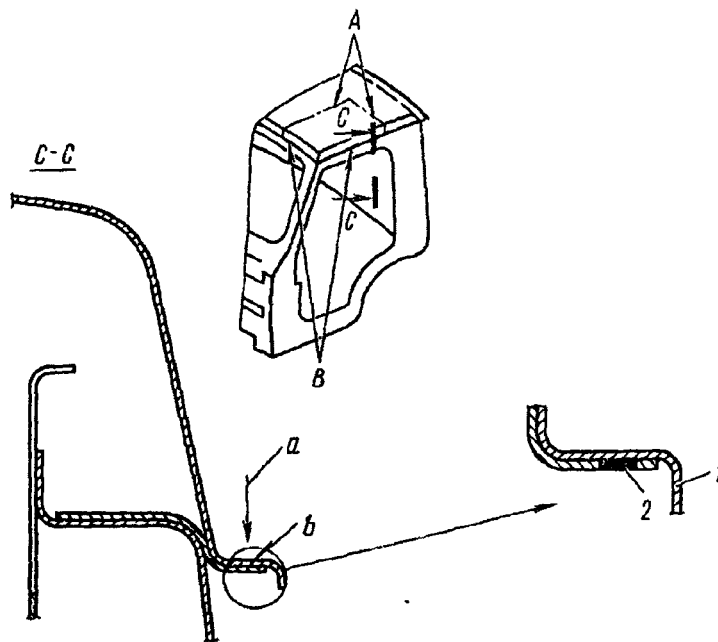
Места отсоединения дефектных деталей и способ приварки ремонтных деталей:
